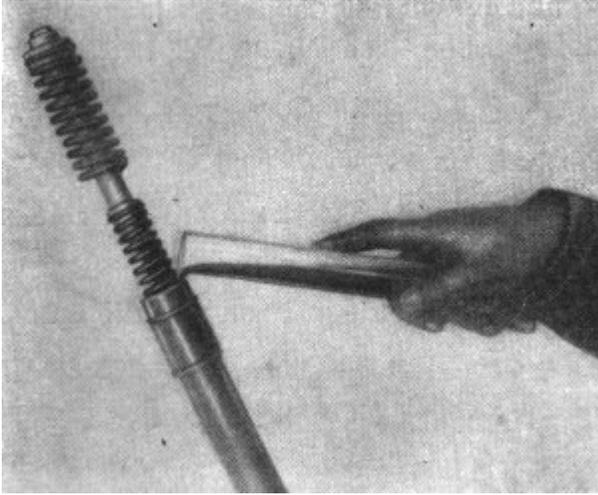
Vor dem Einbau der Teleskoprohre soll das Stoßdämpferöl eingefüllt werden
